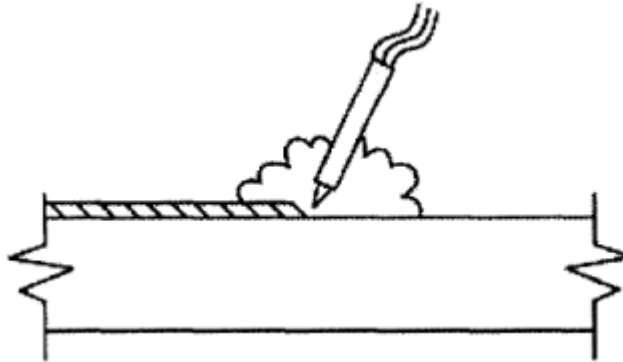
illustration de la soudure à l'arc électrique submergée[9]
